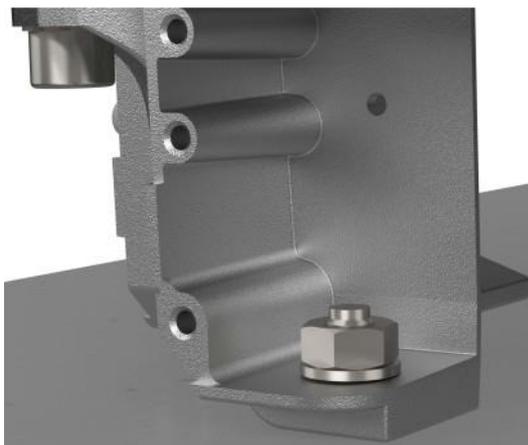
Ladesäulenbefestigung mit Fixanker, Scheiben und Muttern
